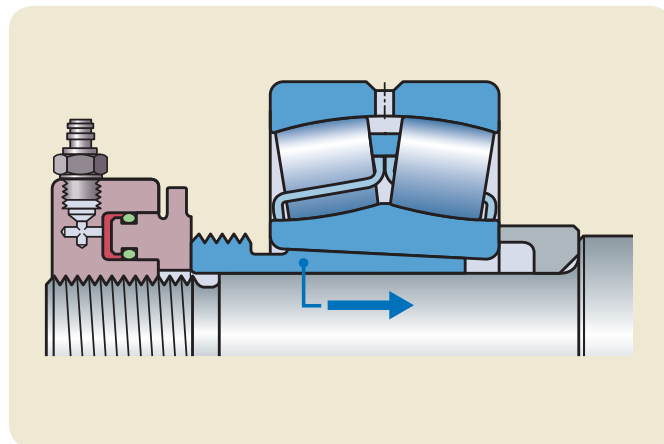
Rodamiento montado sobre un manguito de desmontaje que se empuja entre el rodamiento y el eje.
